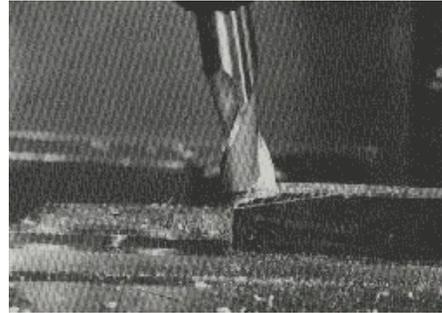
Corte de un ángulo por inclinación de la cabeza de trabajo y utilizando los dientes del extremo de una fresa de extremo plano.
